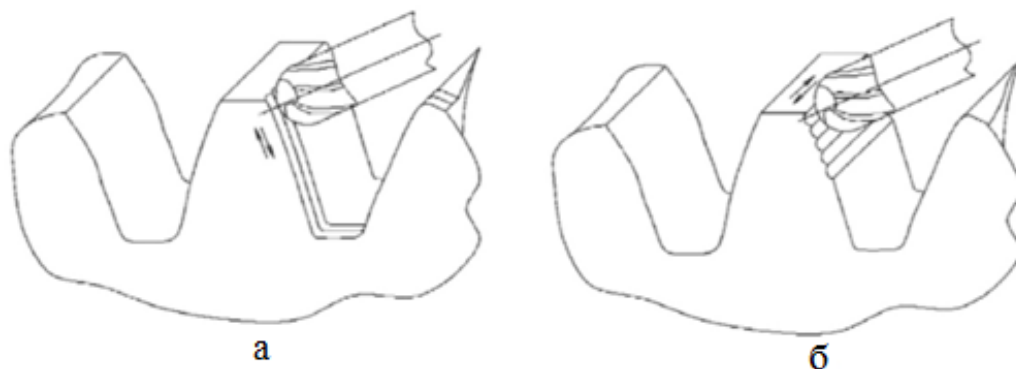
Схема обработки методом высокоскоростного концевой фрезерования:
